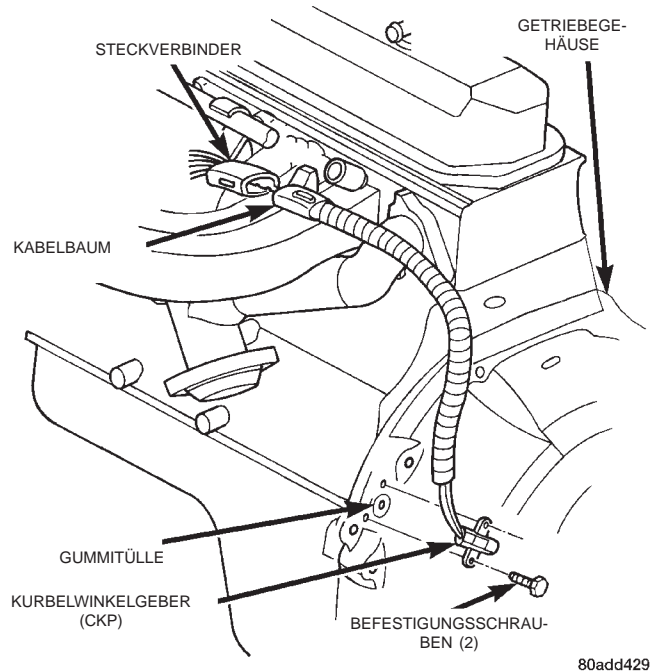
Kurbelwinkelgeber (CKP)—Fahrzeuge mit Schaltgetriebe—Typisch
